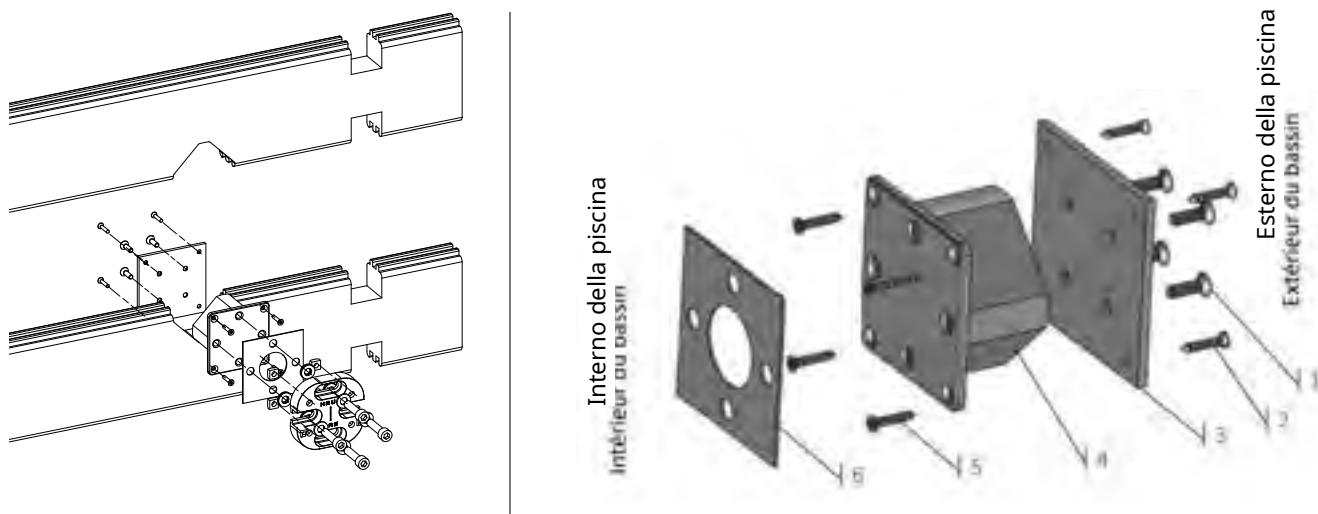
Montaggio dell'unità di supporto cuscinetti
